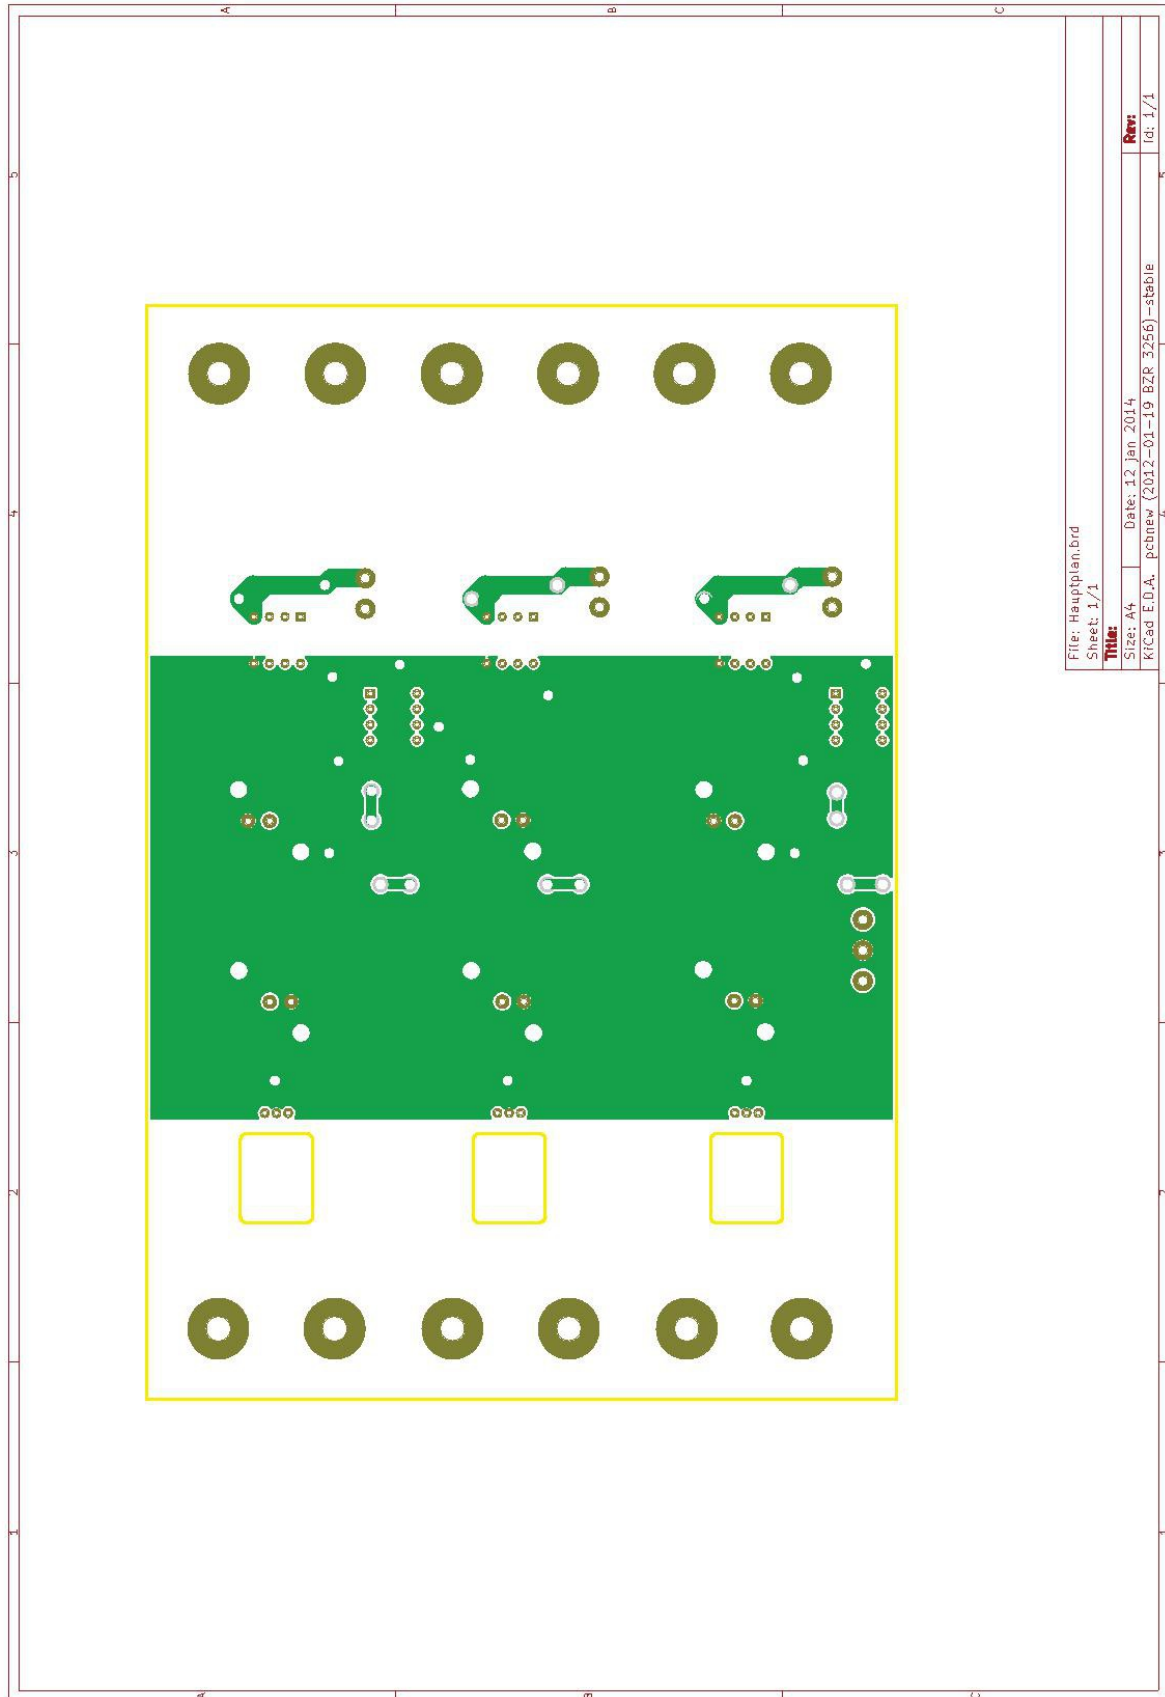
PCB-Layout Rückseite (bottom) der Gruppierungen 1 und 2
